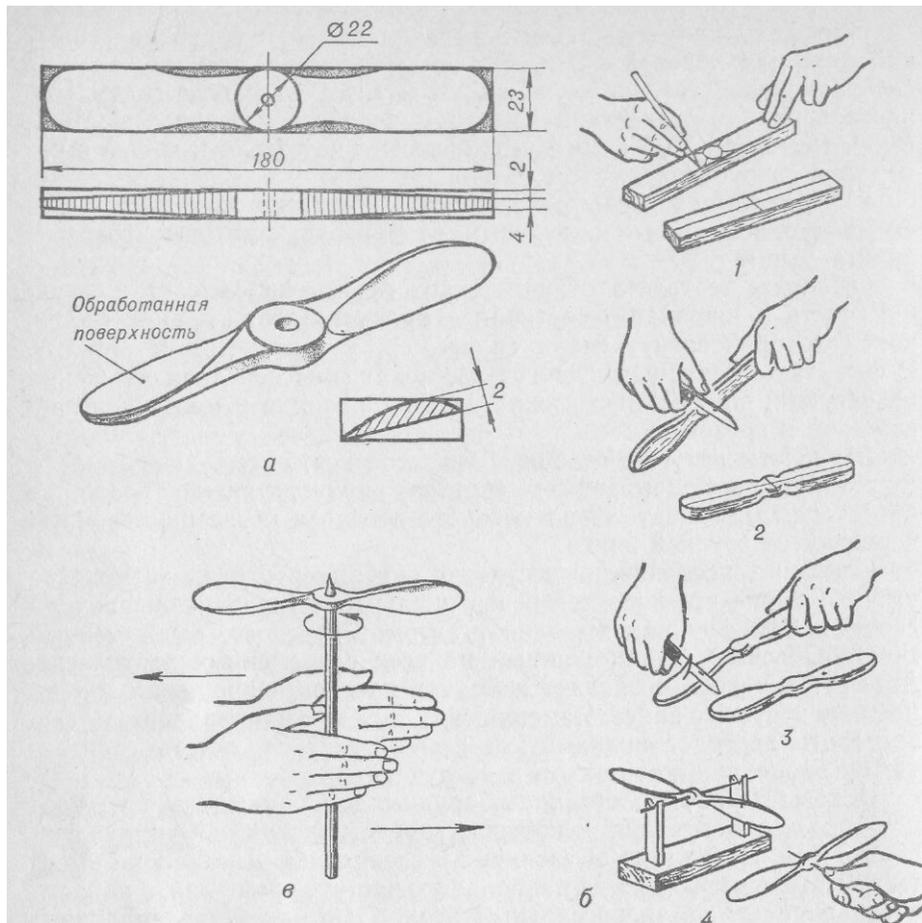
Летящий винт — простейший вертолет «муха»: а — лопасть винта; б — порядок изготовления; в — запуск.
